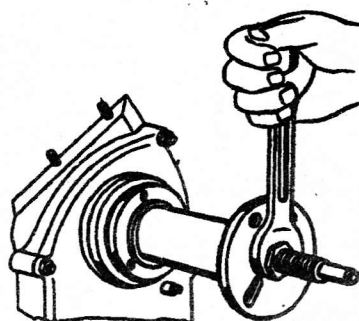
Напрессовка ступицы шкива коленчатого вала с помощью приспособления 16-У-236817
